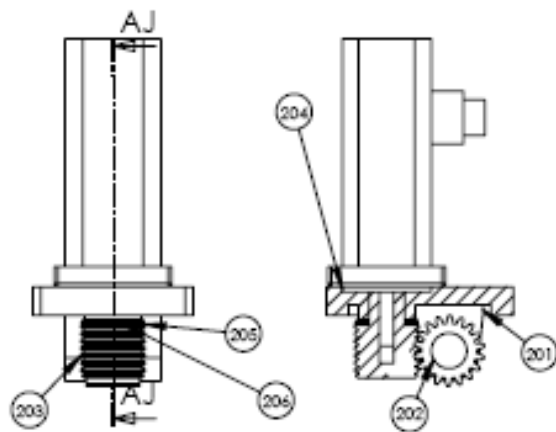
Desenho do mecanismo de elevação do cabeçote.
